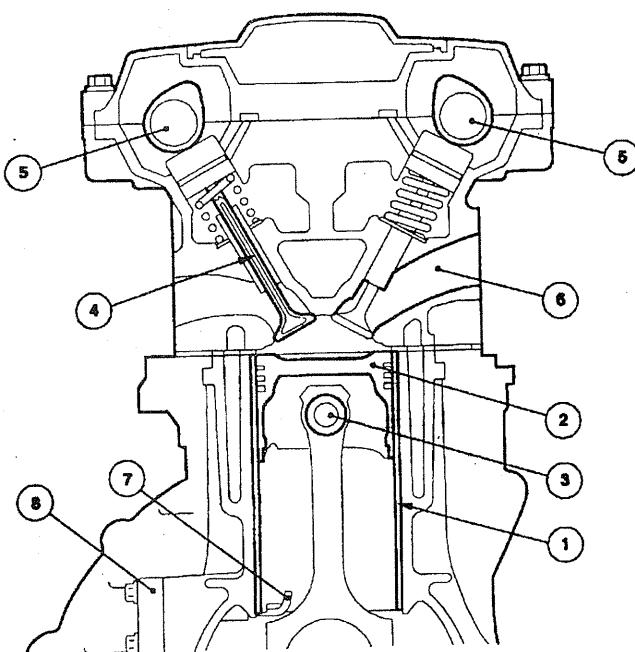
Турбодвигатель (1-гильз цилиндра; 2-поршень; 3-поршневой палец; 4-выхлопной клапан; 5-распределительный вал; 6-впускной клапан; 7-сопло для охлаждения поршня; 8-крышка).
